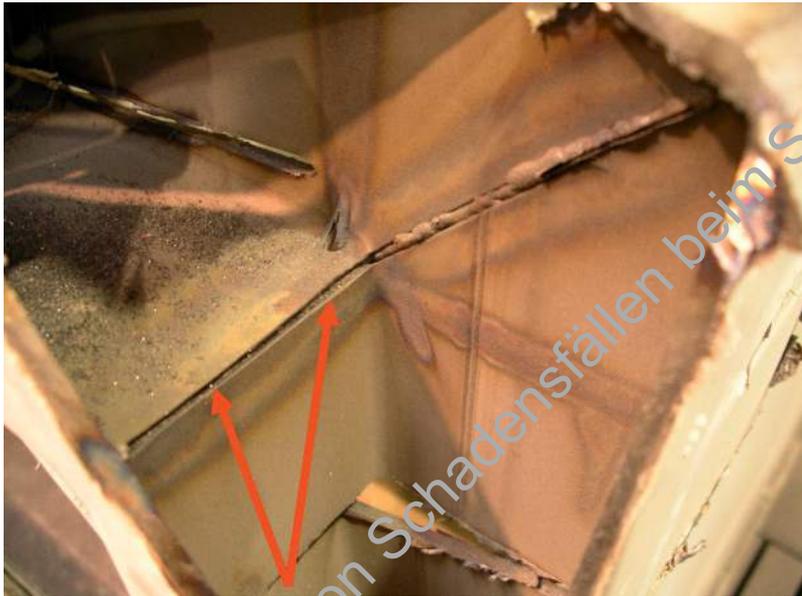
Nicht durchgeschweißte Nähte
